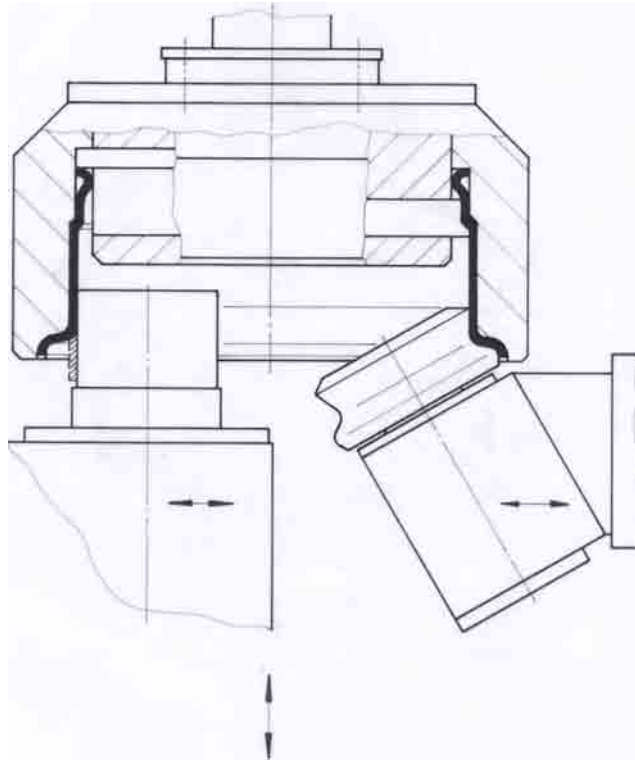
Vista superior do cabeçote, rolos e mandril
